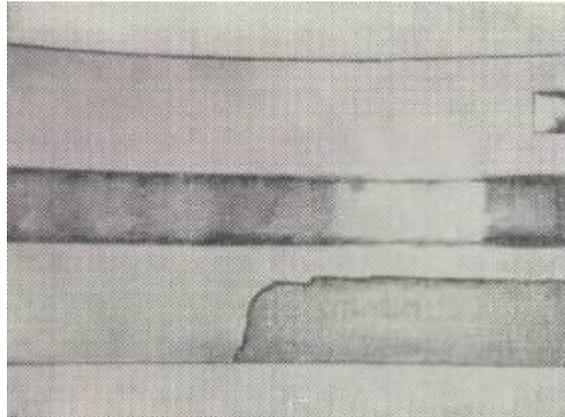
Выкрашивание антифрикционного слоя вкладыша подшипника коленчатого вала двигателя.
